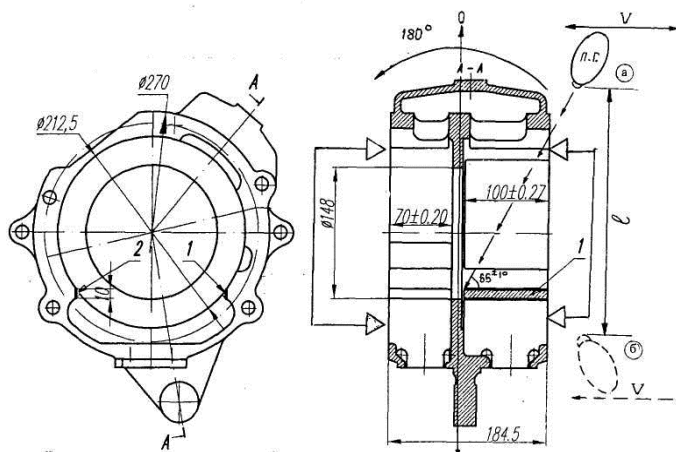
Принципиальная схема термоупрочнения упоров промежуточных дисков корпусных деталей тормоза 1221М: 1 – упрочняемая поверхность остановочного тормоза; Л.Г. – лазерная фокусирующая головка в исходном положении (а);  $v$  – скорость перемещения головки;  $l$  – перемещение головки в новое положение
